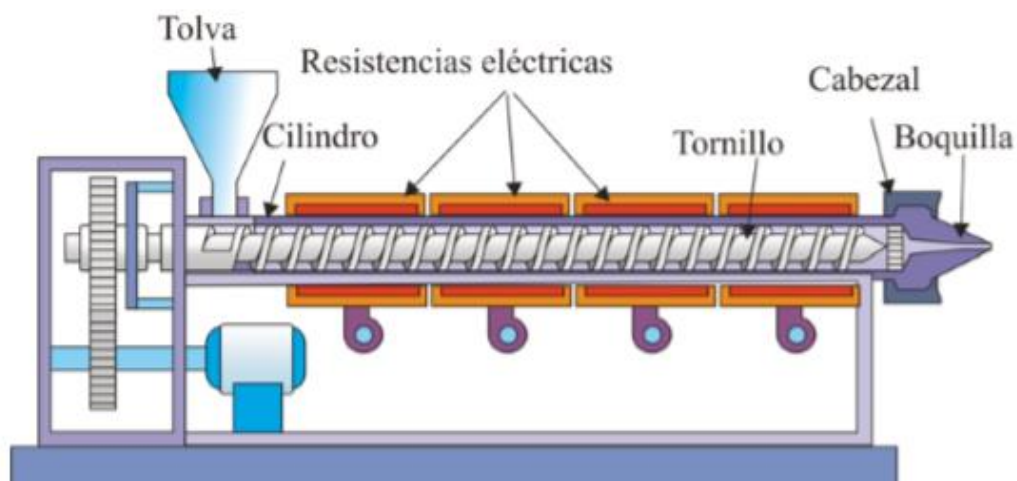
Maquina Extrusora. Fuente. Interempresas Media, 2019
